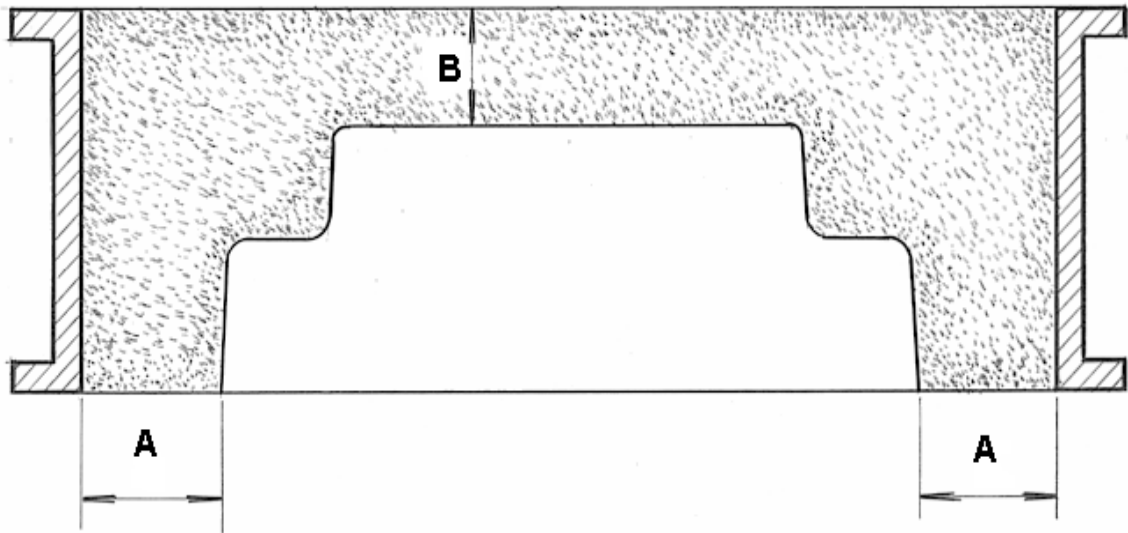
Dimensões num sistema de moldagem cura a frio (máximas).
